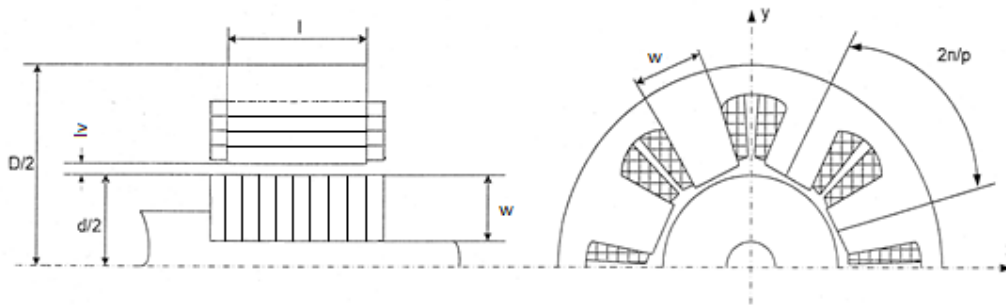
Příklad soustavy aktivních magnetických ložisek. Převzato z [22].
